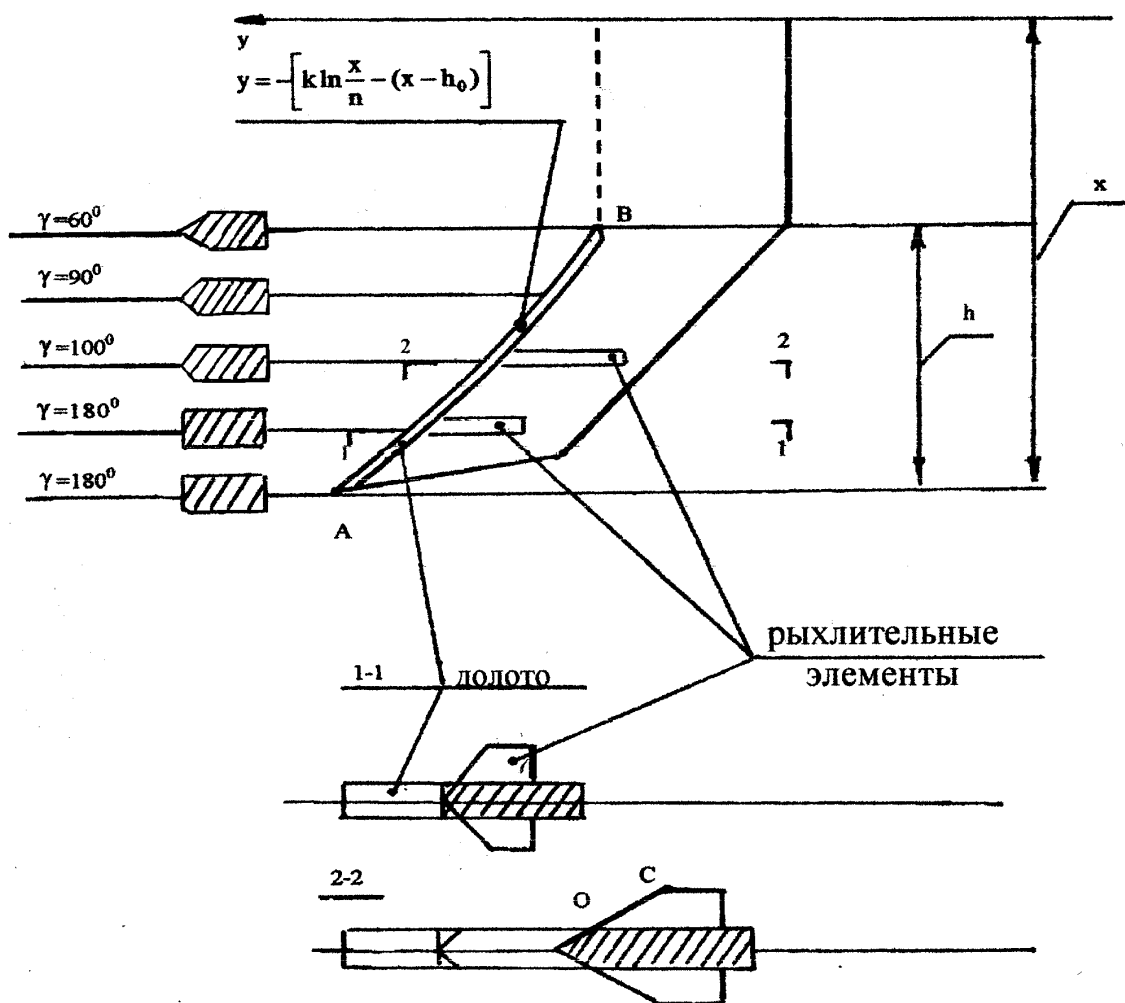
Схема ножа щелевателя с плоскими рыхлительными элементами
